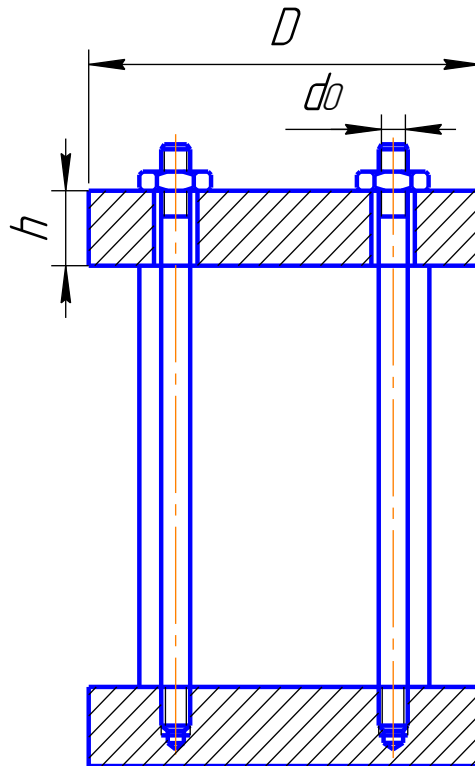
Схема з'єднання пневмоциліндру
